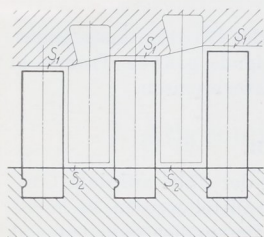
Ausschnitt aus einer Trommelturbine.
